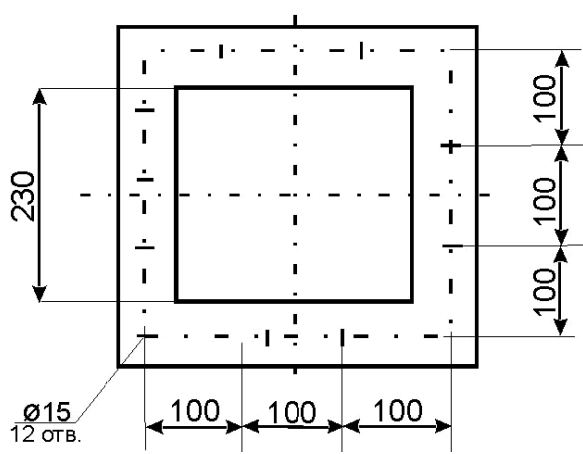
Схема фильтров рукавных типа ФРИП-15; ФРИП-30; ФРИП-180:
